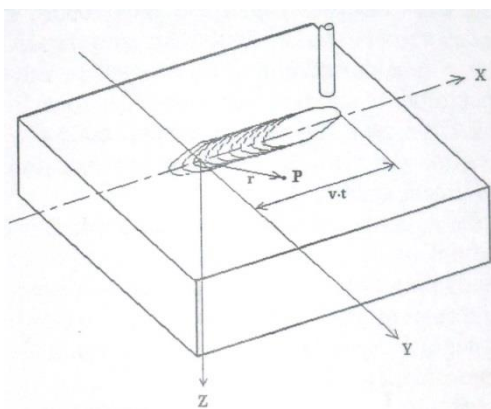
Soldagem sendo realizada sobre a superfície de um corpo (adaptado de Machado, 2000).
